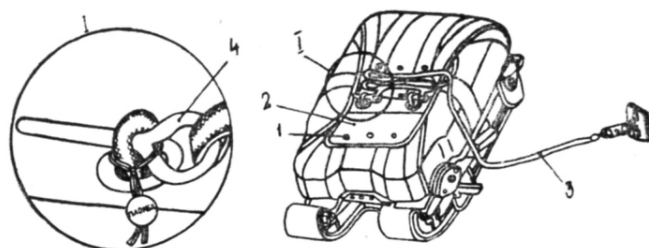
Зачековка клапанов ранца и контровка шпилек:
